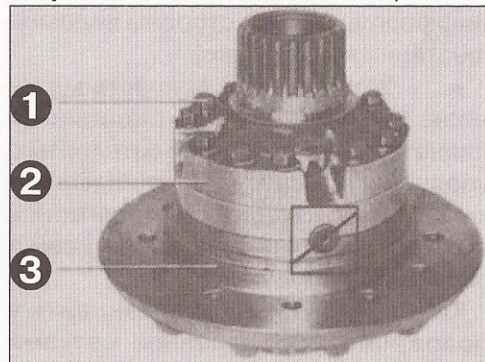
Расположение меток на разъемных частях коробки дифференциала и крестовины.
